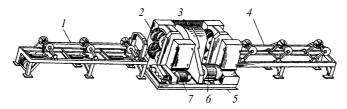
Окорочный станок ОК-63: I – подающий конвейер; 2 – механизм подачи; 3 – окорочная головка; 4 – приемный конвейер; 5 – рама станка; 6 – привод ротора; 7 – привод механизма подачи
